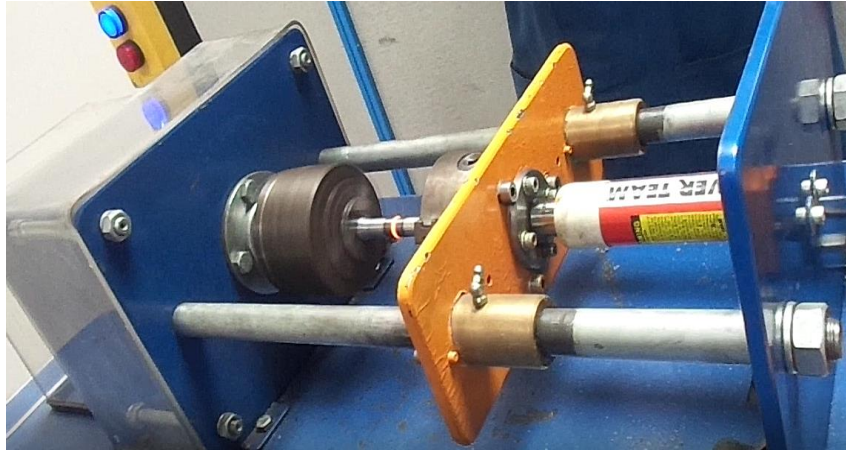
Soldadura por fricción del acero AISI 1018
